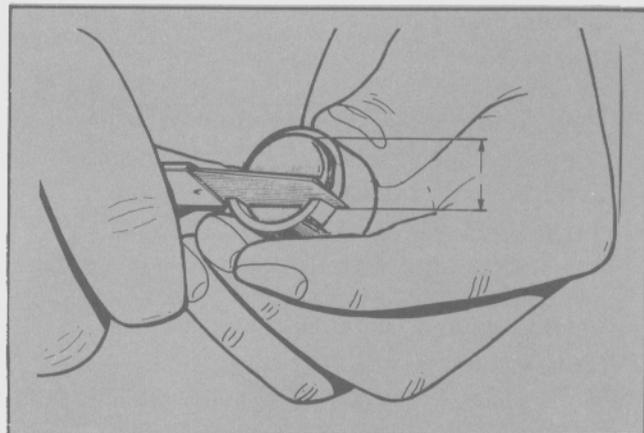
Corte de la boquilla aplicadora de imprimador.
